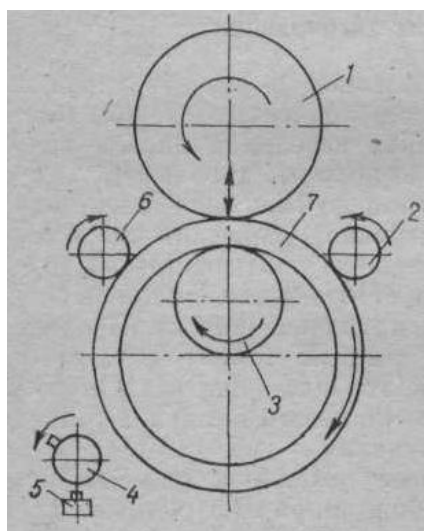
Схема розкочування кільцевих заготовок
